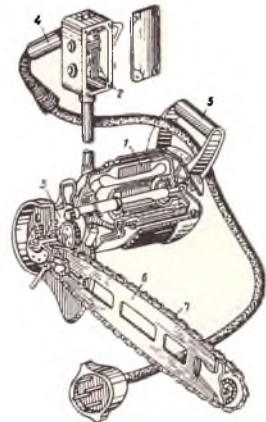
Электропила ЦНИИМЭ К-5: 1 — электродвигатель; 2 — выключатель; 3 — редуктор; 4 — правая рукоятка; 5 — левая рукоятка; 6 — консольная пильная шина; 7 — пильная цепь
